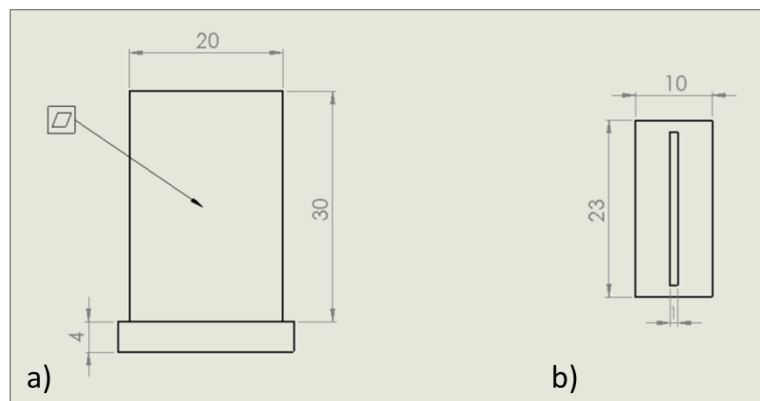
Dessin technique du mur, avec mesure de planéité a) vu de côté ; b) vu du dessus, en mm
